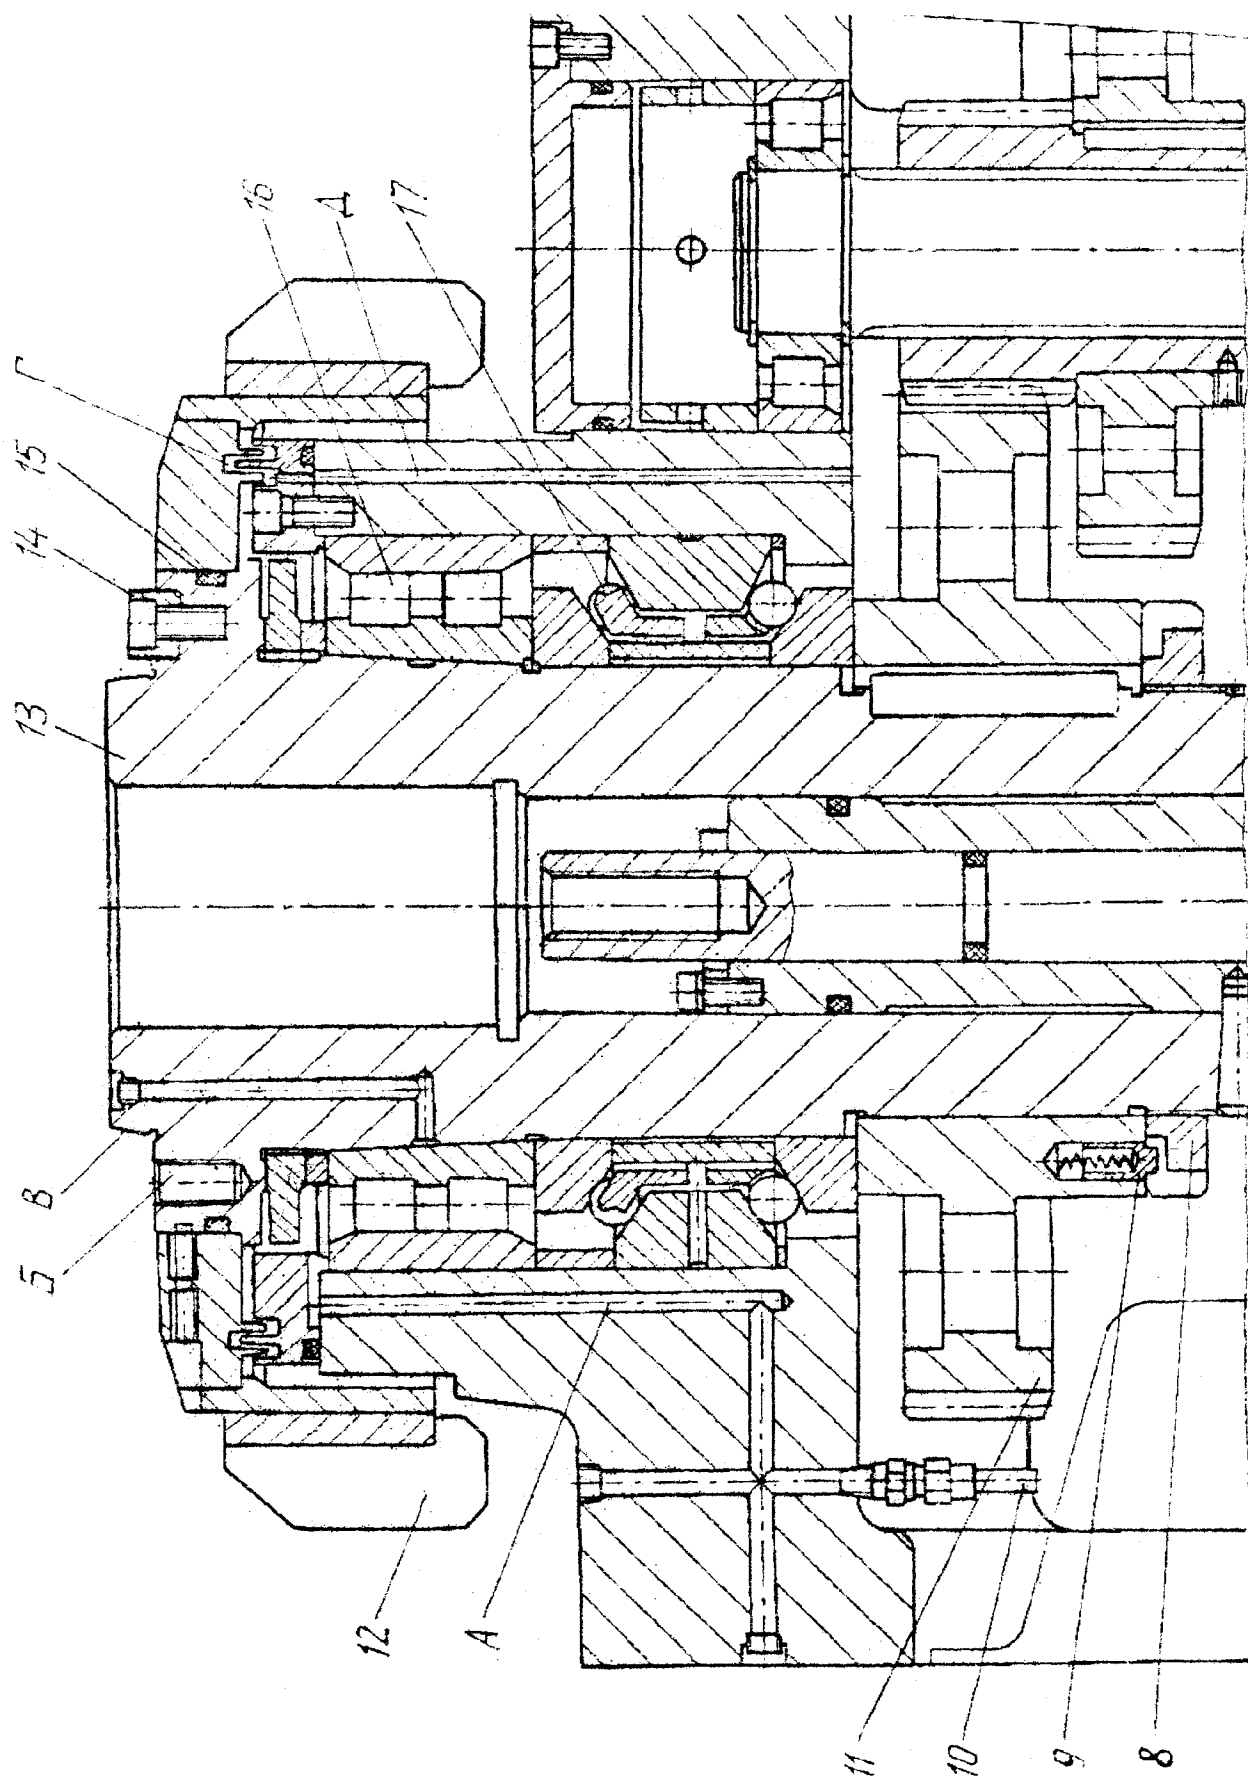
Шпиндельный узел многоцелевого фрезерно-сверлильно-расточного станка
